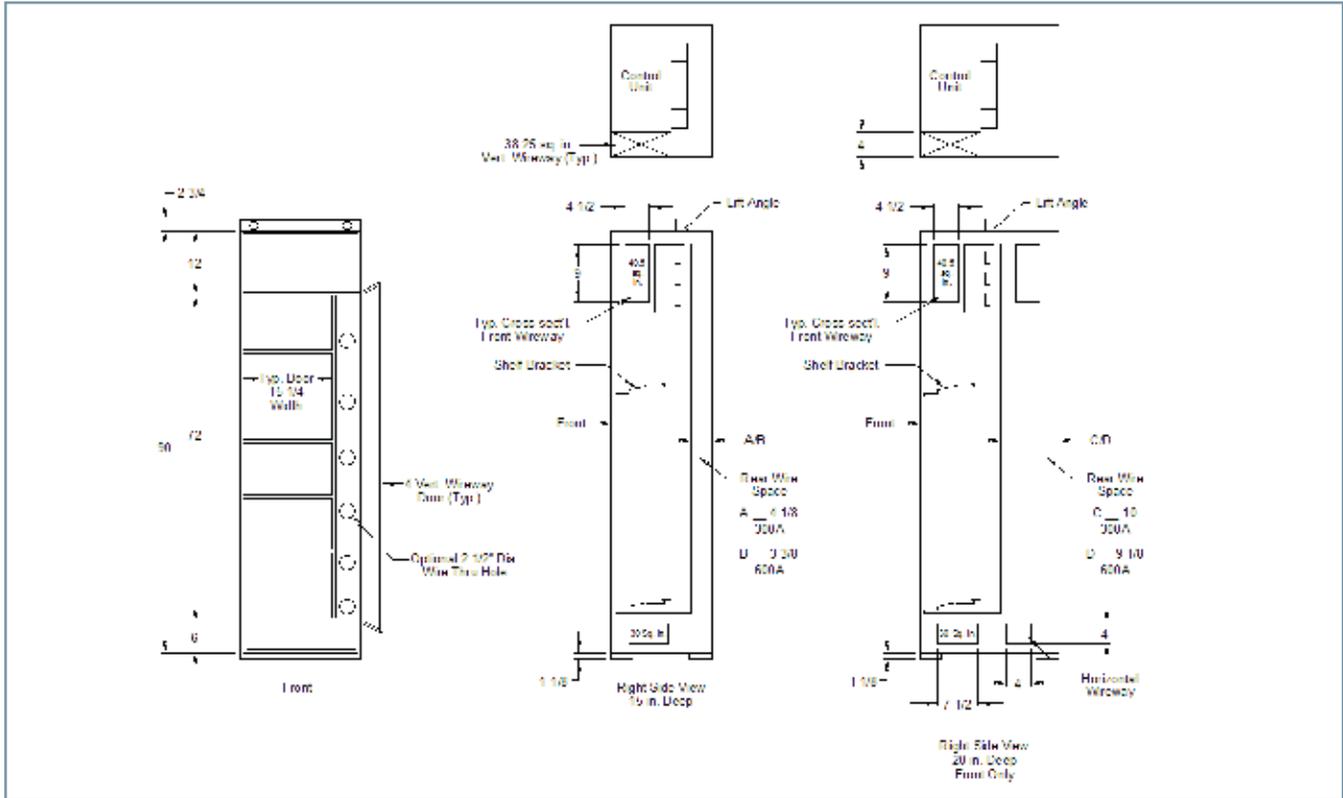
Vista frontal y lateral derecha de dibujos de canaletas de cables
